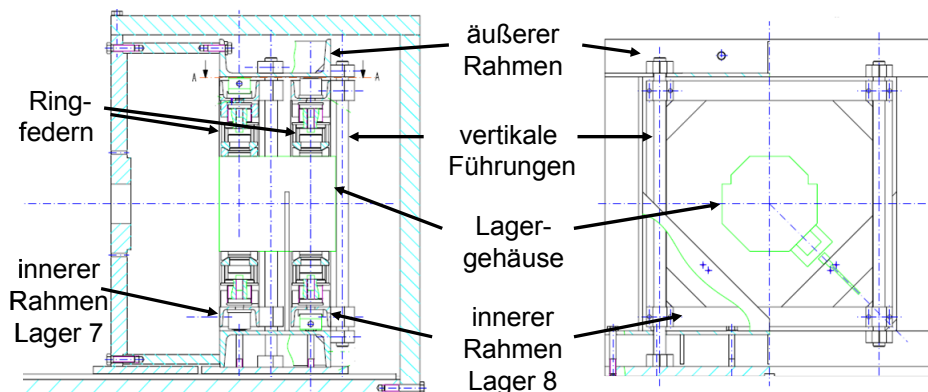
Links: Rahmen Lager 2 und 3 eingebaut; Rechts: Rahmen montiert ohne Ringfedern einer Stahlplatte mit 12 Schrauben (M16) befestigt. Zusätzlich ist in der Stahlplatte eine Nut eingebracht, die der Fixierung des Rahmens in der Axialrichtung des Prüfstandes dient. Die Stahlplatte ist wiederum mit 8 Schrauben (M16) in den Befestigungsnuten des Prüfstandes montiert. In die oberen Elemente des Rahmens sind außen mittig in den U-Profilen Versteifungsbleche quer eingeschweißt, um eine Erhöhung der Biegesteifigkeit zu erzielen. Im unteren Segment des Rahmens sind leicht außermittig des Profils zwei Dreiecke eingeschweißt, die sowohl zur Montage von Sensoren dienen, sowie die Funktion einer Aussteifung erfüllen. Die Bleche sind massiv mit einer Stärke von 10 mm ausgeführt, um den Einfluss der Eigendynamik der Sensorhalterung auf die Messergebnisse gering zu halten. Aufgrund dieser Konstruktion besitzt der äußere Rahmen eine anisotrope Steifigkeit. Bei einer späteren Messung ergaben sich die Rahmensteifigkeiten an der oberen vertikalen Position zu 200 kN/mm . Die horizontalen Steifigkeiten wurden jeweils mit 2 MN/mm berechnet. Für die untere vertikale Steifigkeit ergab eine Abschätzung 10 MN/mm . Bei der Verwendung mit Ringfedern wirkt sich die Anisotropie jedoch kaum aus.
